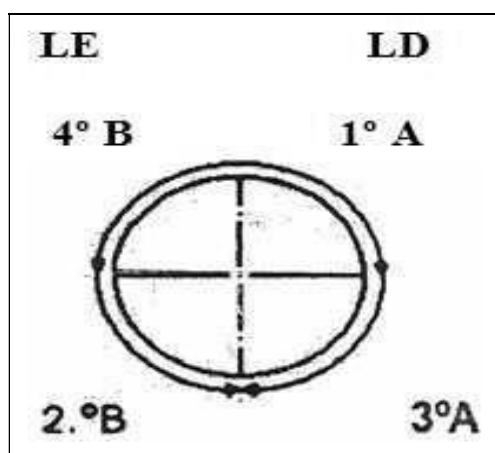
Sequência de soldagem (dois soldadores)
